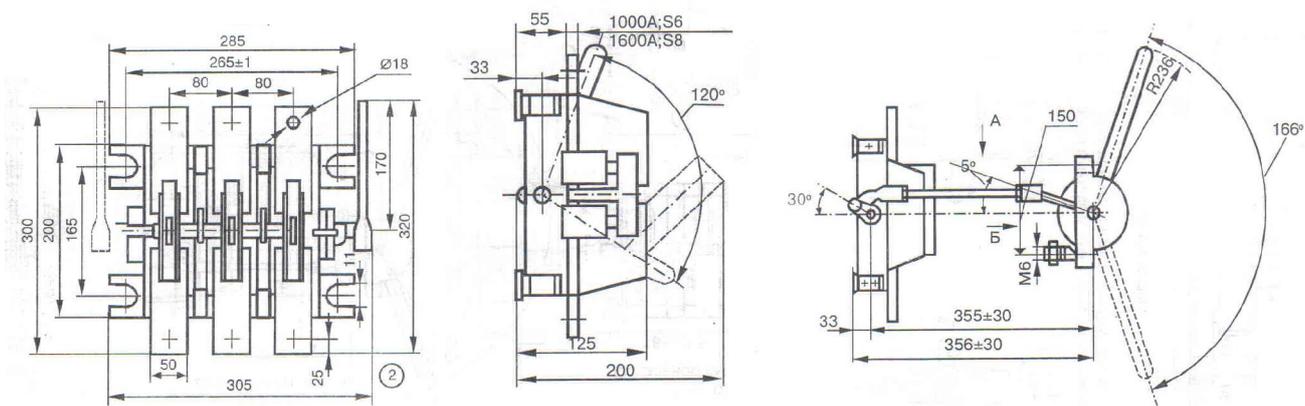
Выключатель-разъединитель трехполюсный серии PE19 с боковой рукояткой справа
